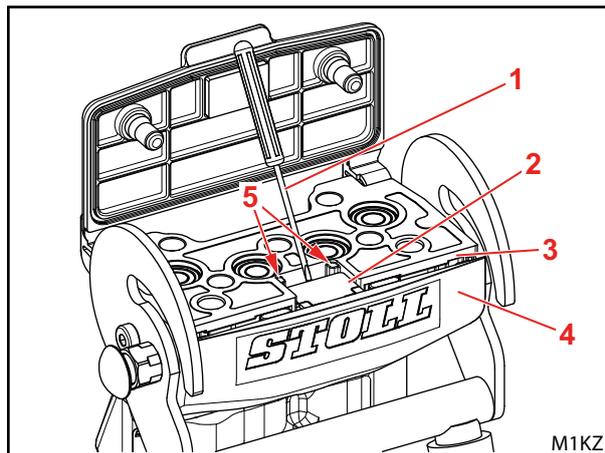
Parte inferiore Hydro-Fix (senza impianto elettrico) montato
